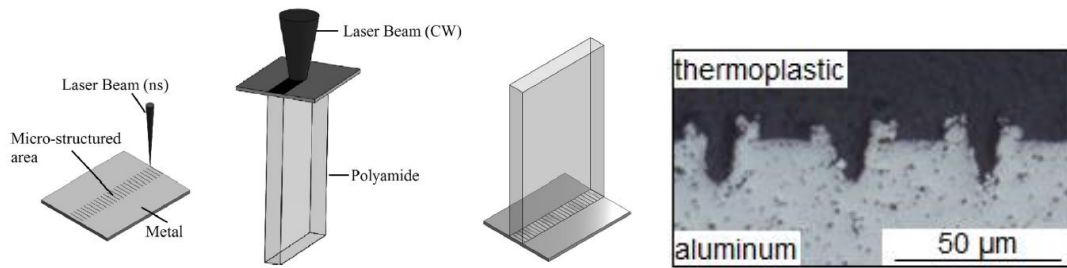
Procédure d'assemblage pour former un joint soudé en T [65] et microstructure d'un joint aluminium / thermoplastique [67]
